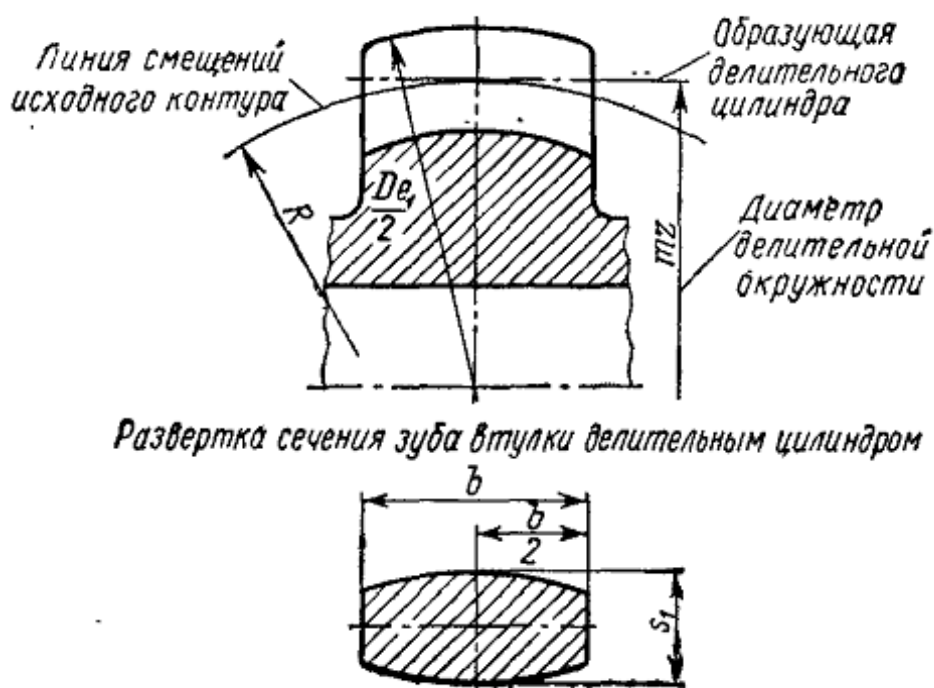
Геометрические размеры бочкообразного зуба зубчатой полумуфты
